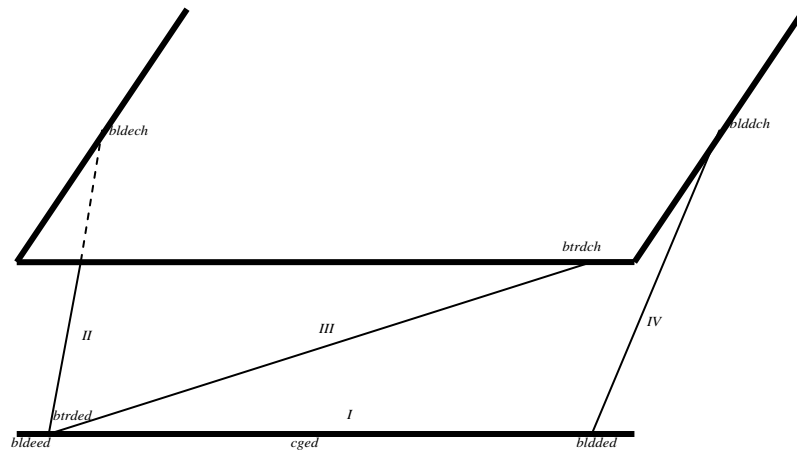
Detalhe do chassi, eixo rígido dianteiro e barras longitudinais e transversal
